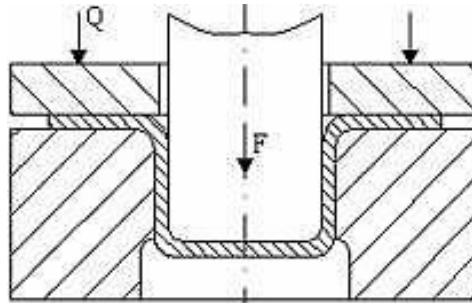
Emboutissage à l'aide d'un poinçon à fond plat.
